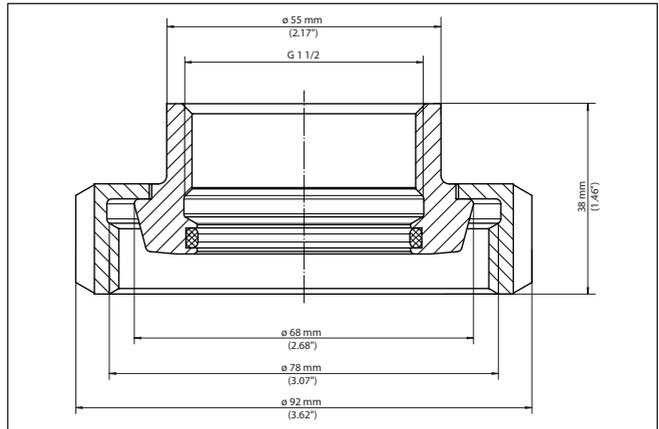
Medidas adaptador de rosca G1½ (DIN 3852-X) sobre união roscada de tubo DN 50 (DIN 11851) PN 16
